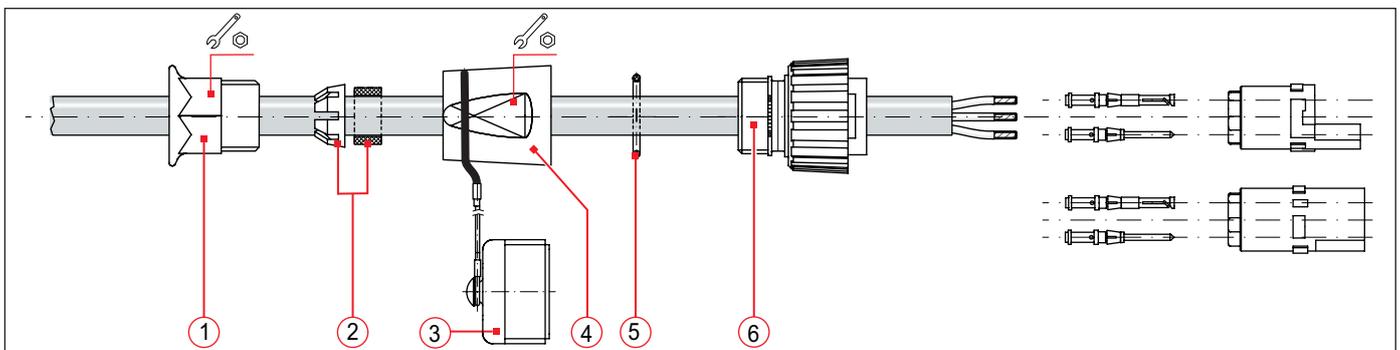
Beispiel für Stecker mit Gewinde, Endgehäuse und Verschraubung (gilt analog auch für Dosen mit Gewinde)
